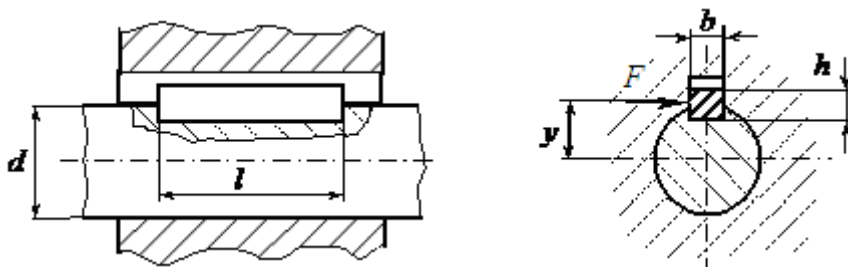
З'єднання деталей за допомогою призматичної шпонки
